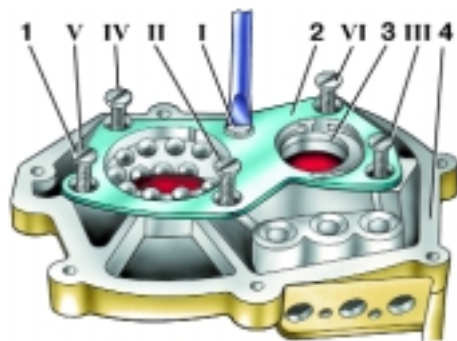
Снятие и установка пластины крепления подшипников: 1 – винт; 2 – пластина; 3 – заднее внутреннее кольцо подшипника первичного вала; 4 – картер; I-VI – последовательность затягивания винтов при сборке
